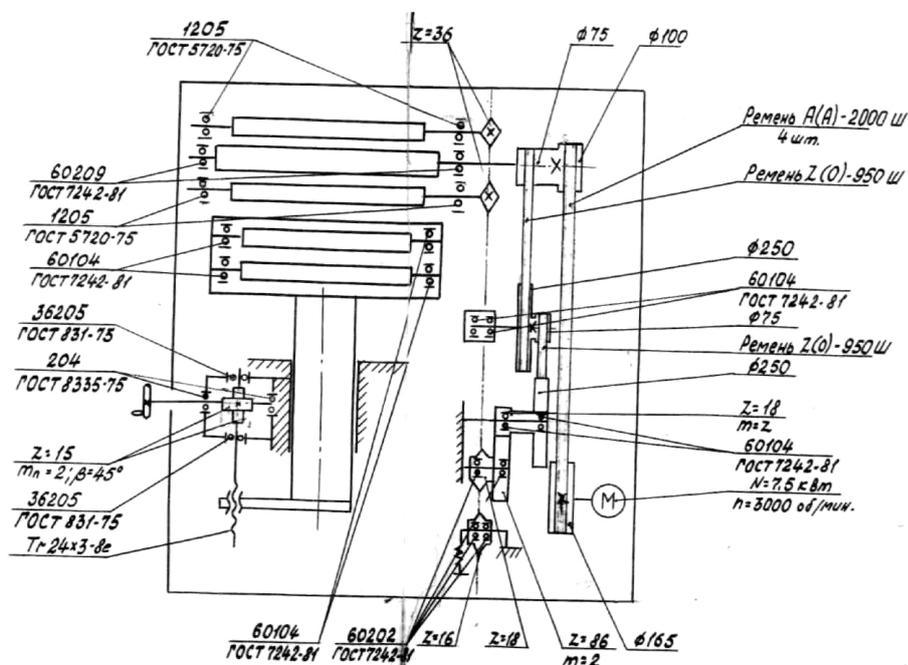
Схема совмещенная кинематическая и расположения подшипников.
